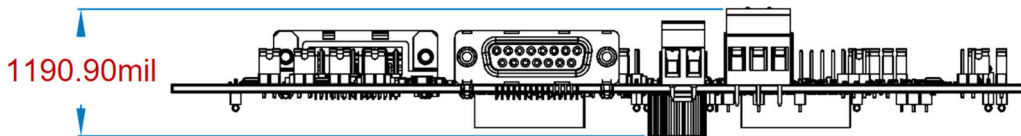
BP-AM2BLDCSERVO PCB 模组 - 前视图/后视图
